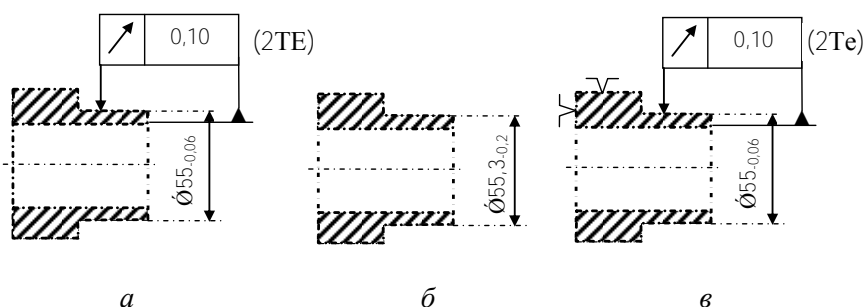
Эскизы детали (а), заготовки (б) и механической обработки (в)
